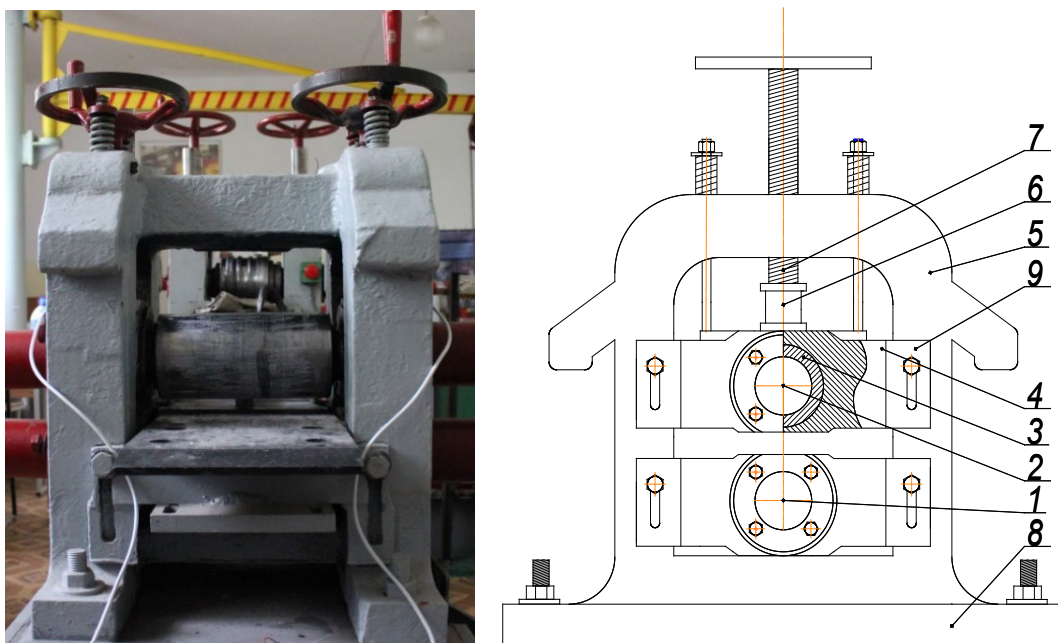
Конструкція робочої кліті лабораторного стану 125×250
